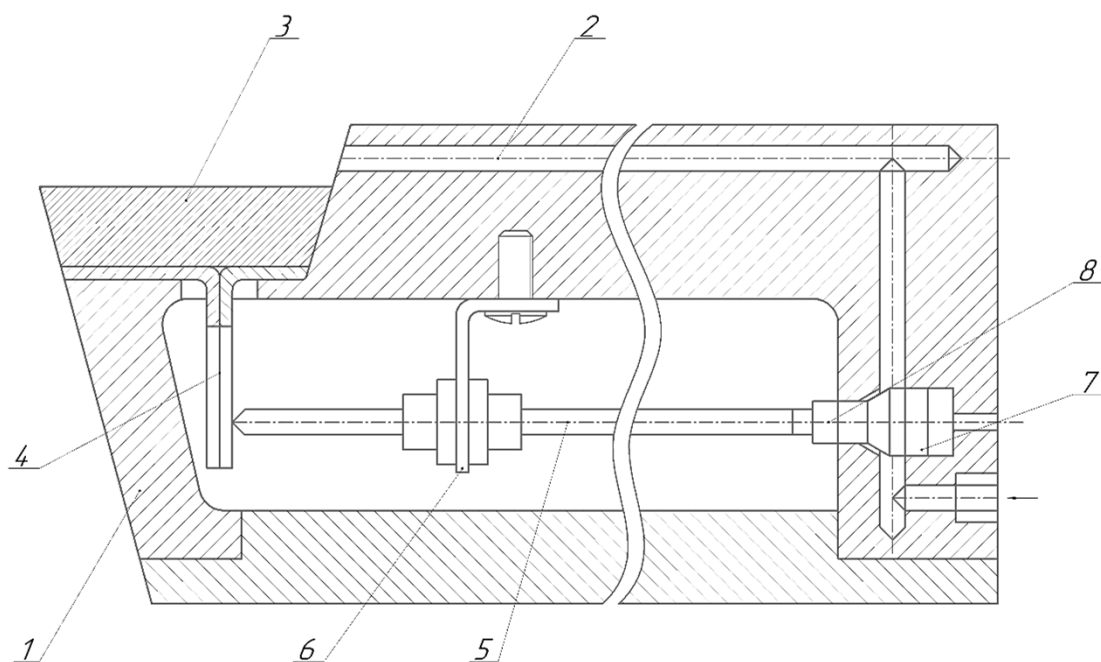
Конструктивная схема предлагаемого металлообрабатывающего инструмента
